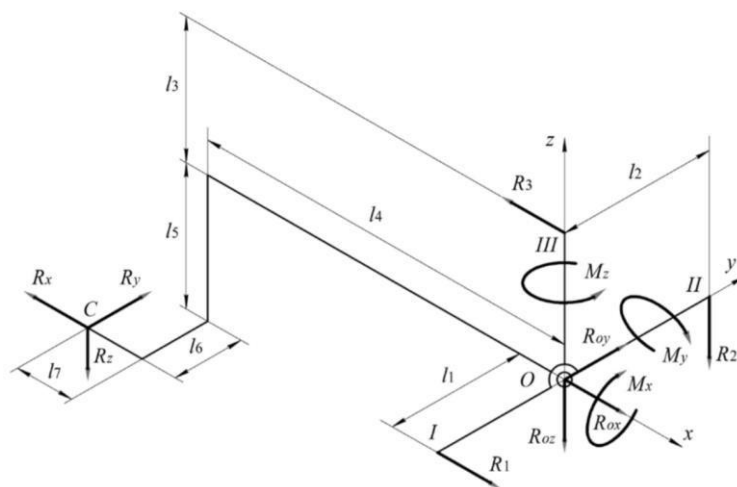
Розрахункова схема динамометричного модуля
